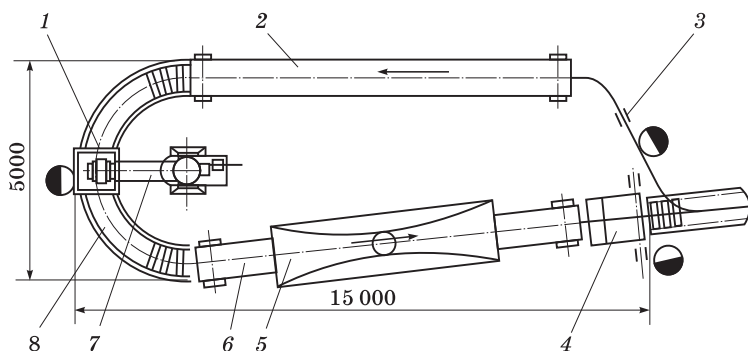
Схема механизированной линии для изготовления стержней из ХТС
